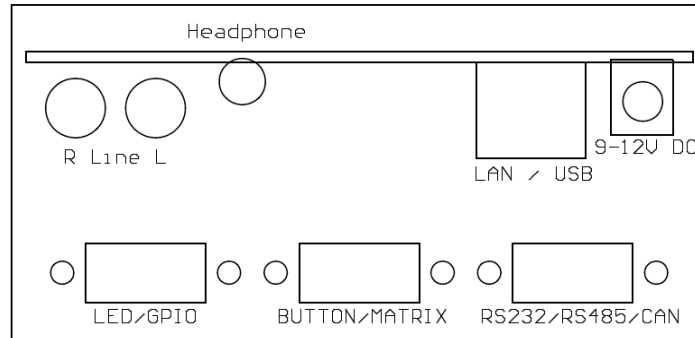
Fallguy ULTRA Carrier Board Rev.I und ULTRA Casing - Abmessungen
